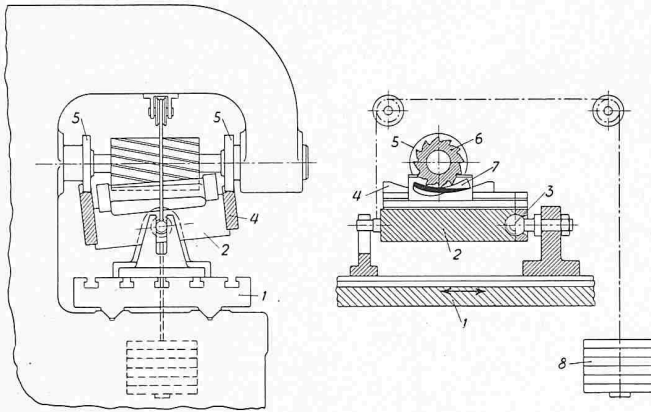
Vorrichtung zum Fräsen von Turbinenschaufeln. 1 Tisch, 2 Wippe, 3 Kugel, 4 Schablonen, 5 Führungsrollen, 6 Walzenfräser, 7 Turbinenschaufel, 8 Anpressgewicht
